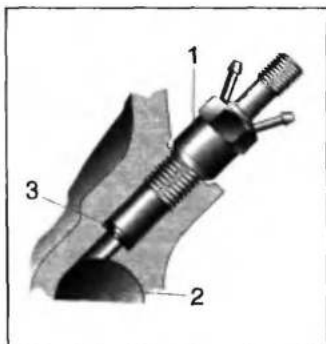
Установка форсунки с экранирующей противопригарной шайбой: 1 — форсунка; 2 — вихревая камера; 3 — противопригарная шайба
